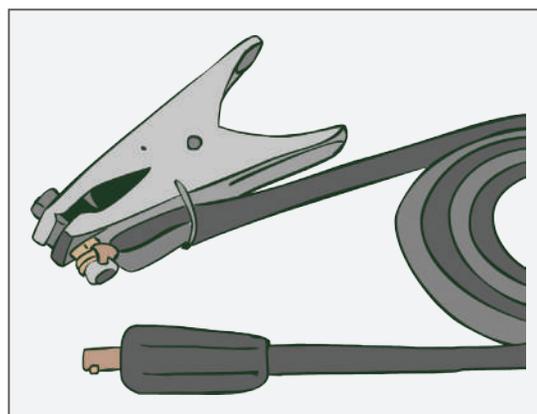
B - Cabo de soldagem unido à garra de aterramento
